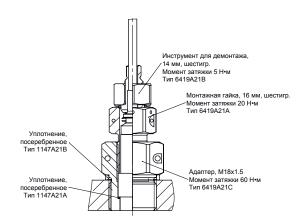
Установка датчика с помощью переходника Типа 6419A21C и инструмента для демонтажа Типа 6419A21B для датчика с использованием разъема LEMO или свободными концами
